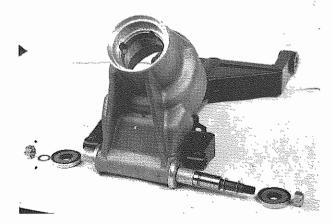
Montare il portamozzo al braccio sospensione Assembling hub holder to suspension arm
